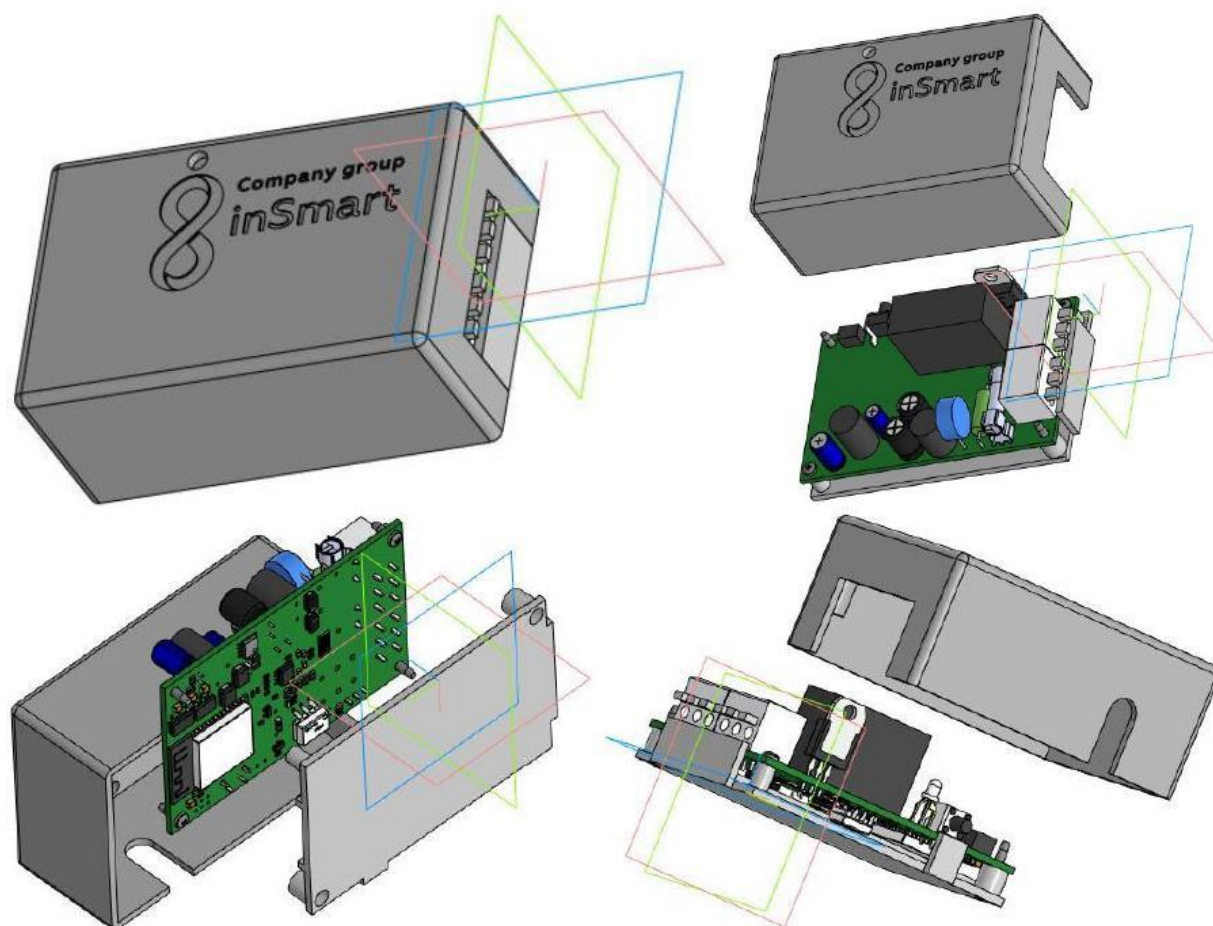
3D - модель корпусу бездротового комутатора навантаження
